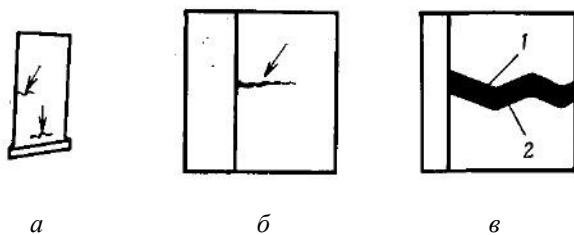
Индикаторный рисунок усталостных трещин на РЛ компрессора:
